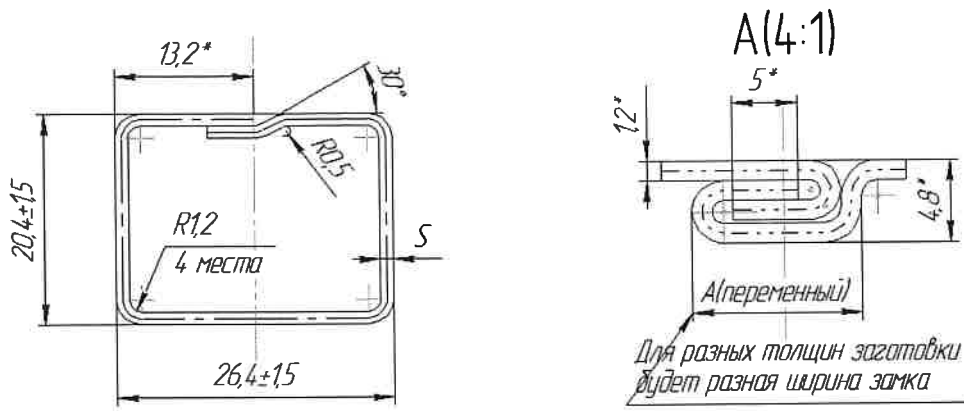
Труба с гофрами (размер заготовки 90 мм)
